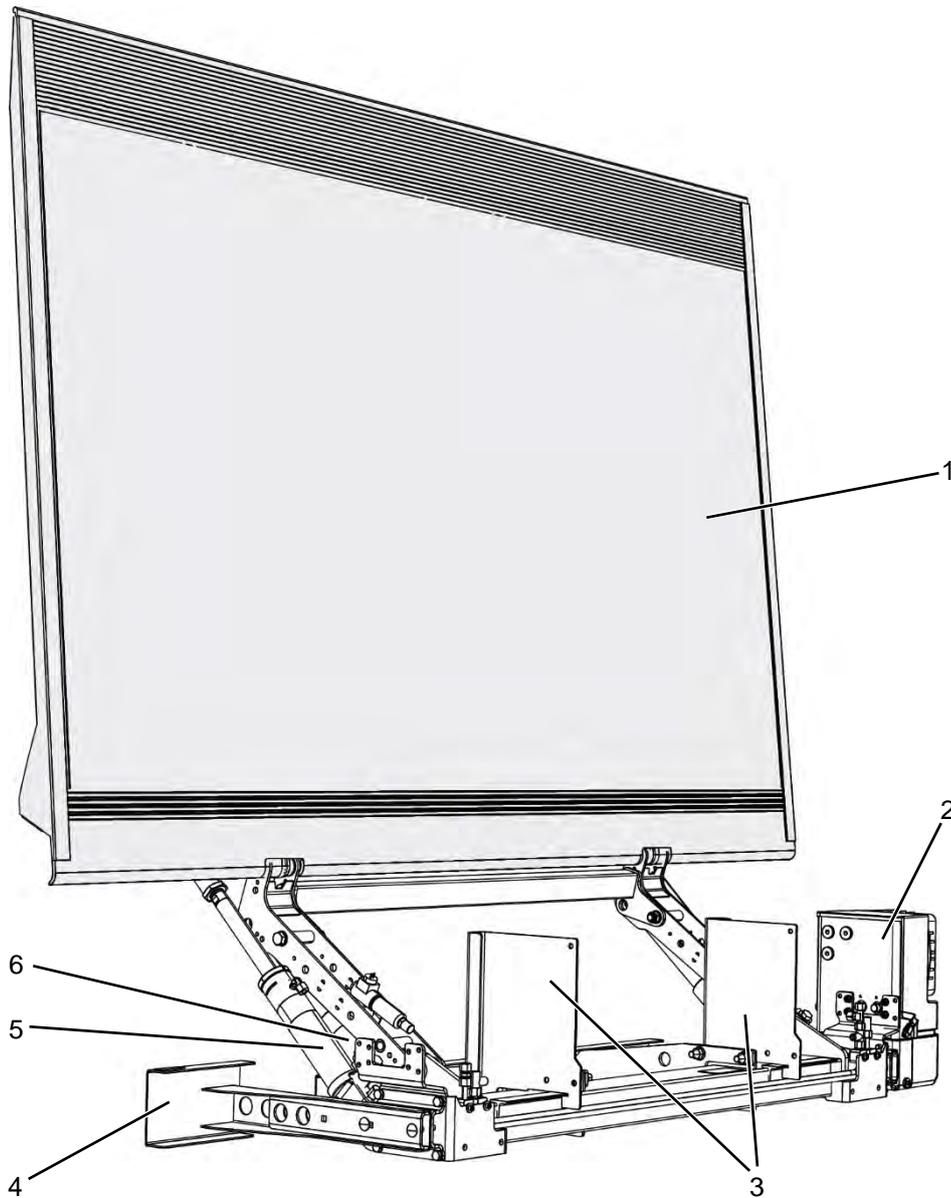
Подъемно-погрузочная платформа с платформой и поворотным агрегатом
